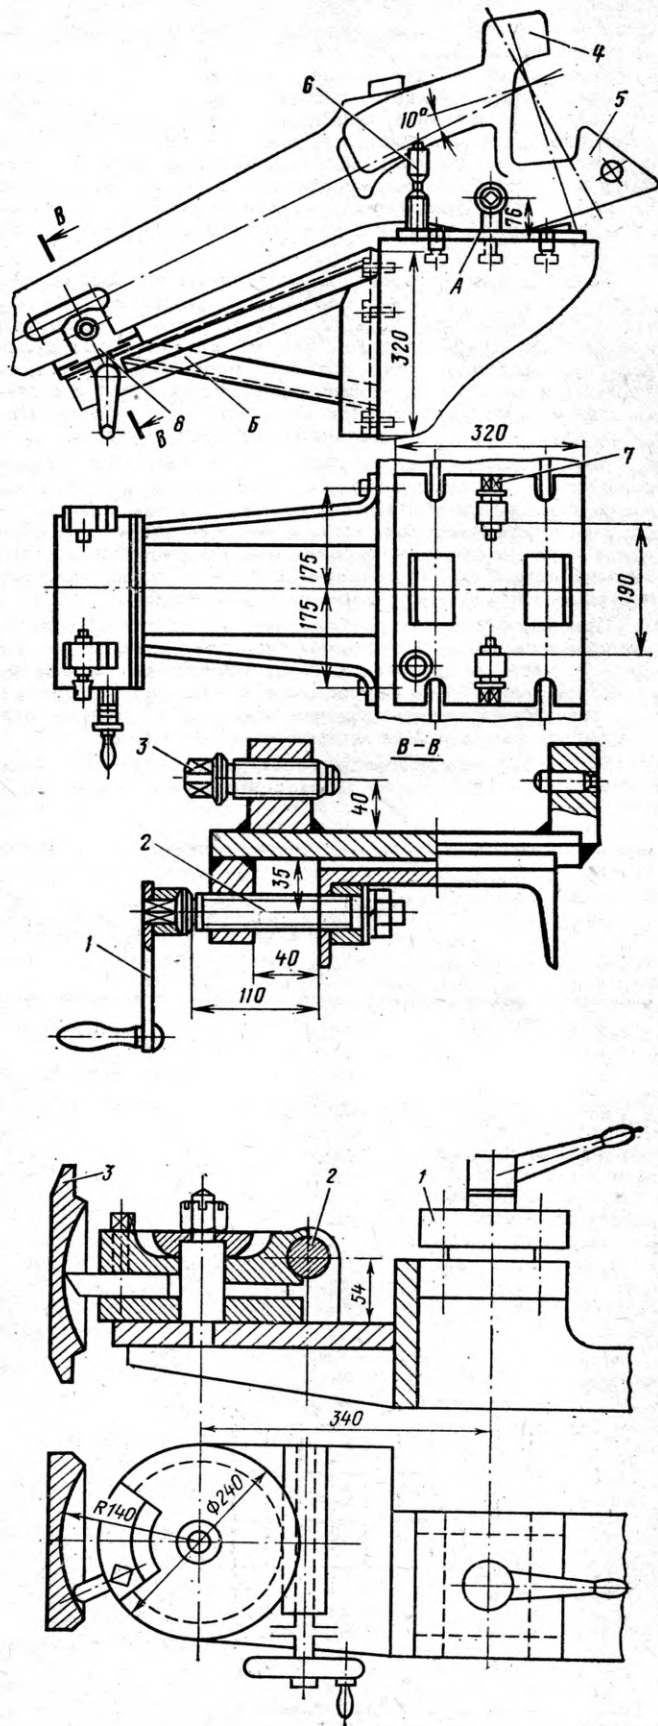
Приспособление для обработки наплавленной сферической поверхности упорной плиты автосцепки:
